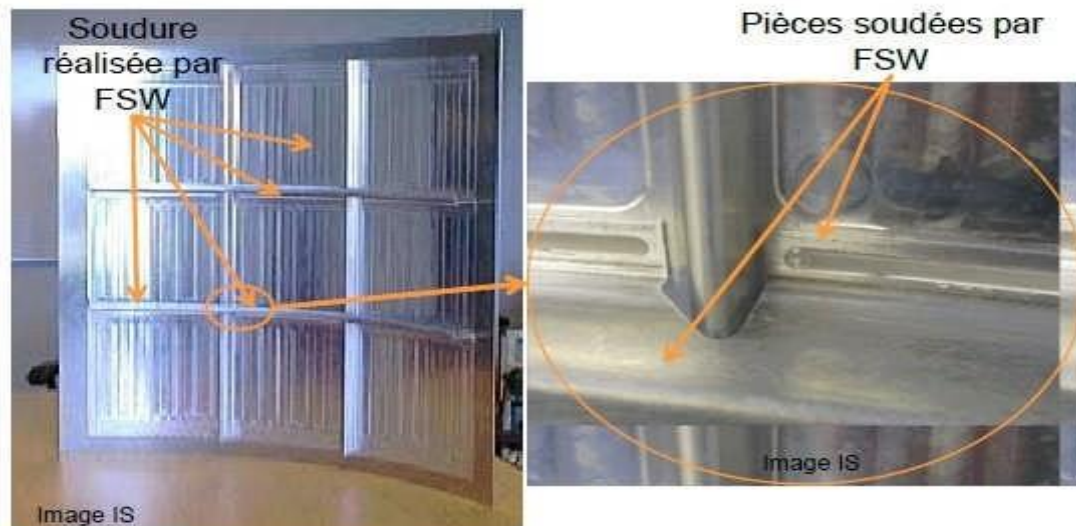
Voilure d'avion soudée par FSW [19].
